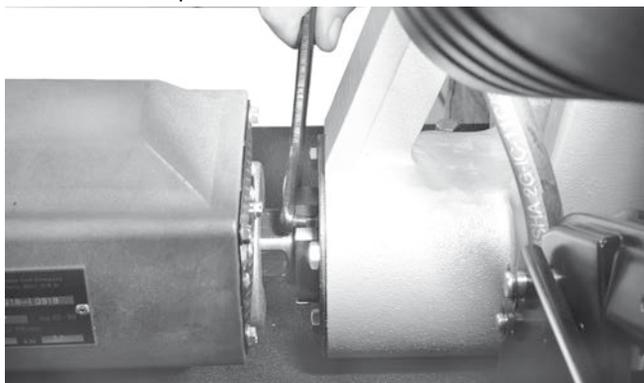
Откручивание и снятие гайки крепления приводного вала
